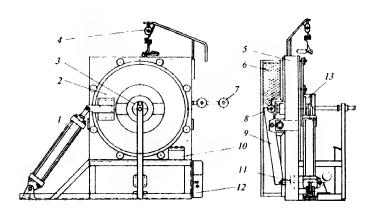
Калибровочный пресс: 1— натяжные кулачки; 2— калибрующее устройство; 3— экспентрик; 4— плита; 5— пневмопилиндр; 6— рама
